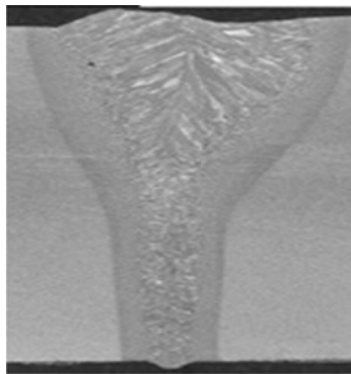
Микроструктура сварного соединения, полученного лазерной сваркой
